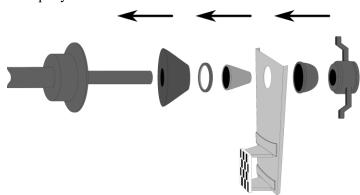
Порядок установки калибровочной пластины с мишенью на вал на втором этапе калибровки
